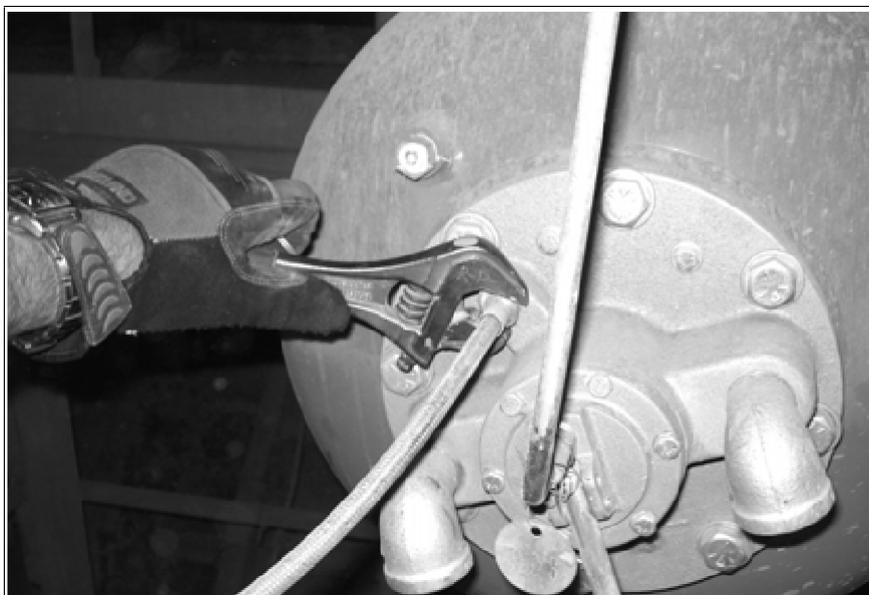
Raccordement de la conduite d'alimentation en air comprimé
